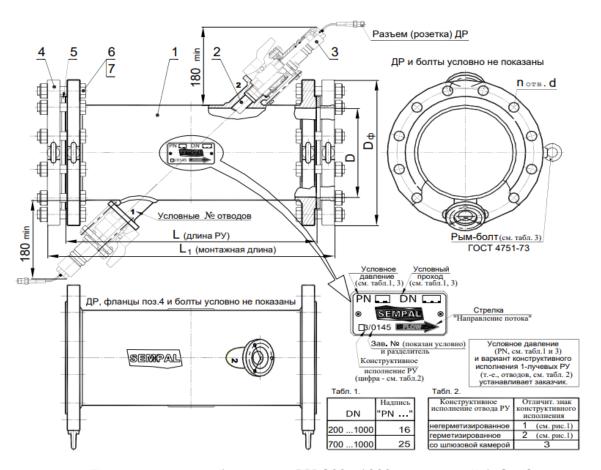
Исполнения (1 и 2) РУ-200...1000 с резервными (стандартными) ДР
